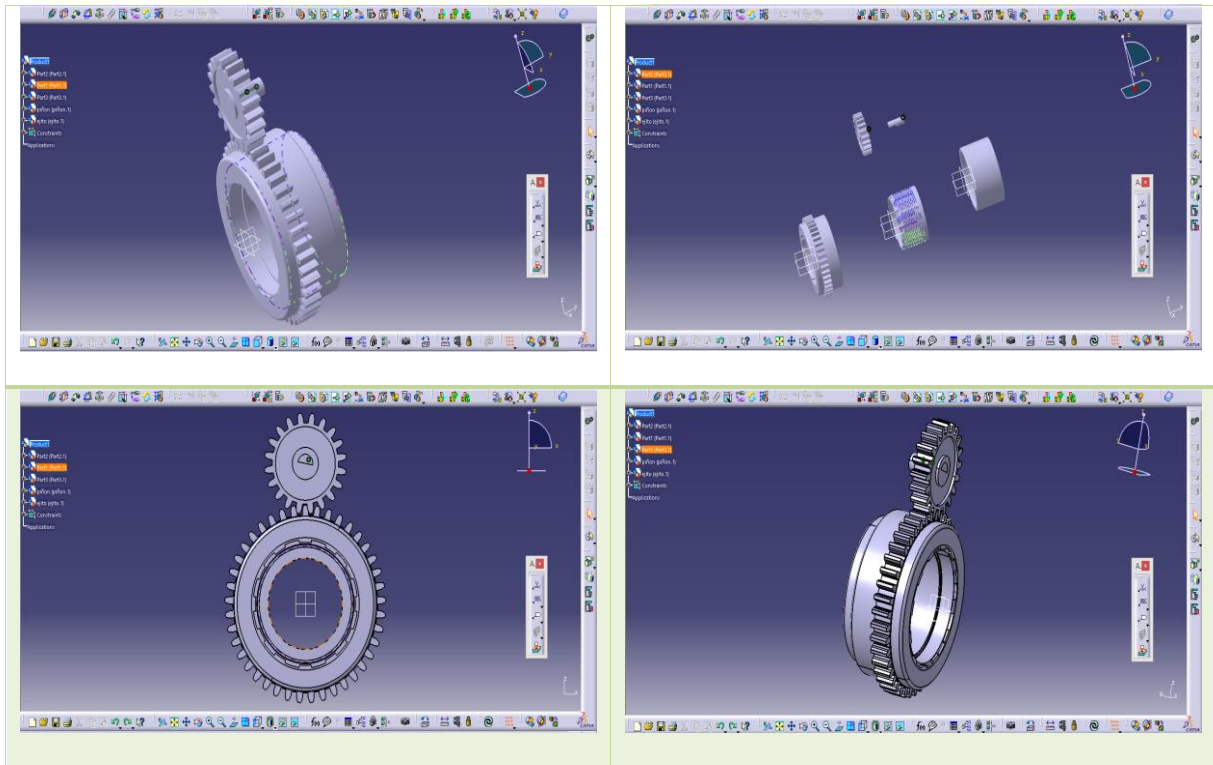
Vistas del modelo CAD del actuador de Ball Screw
